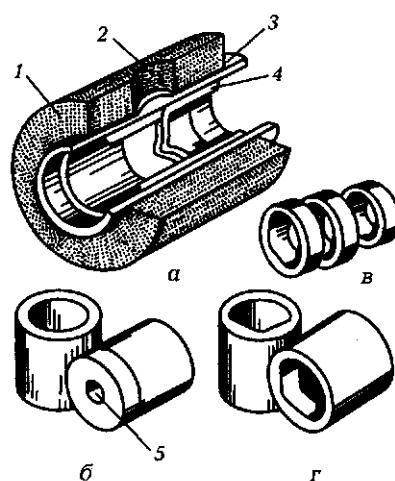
Патрон ПА (а) и детали к нему для термитной сварки:
